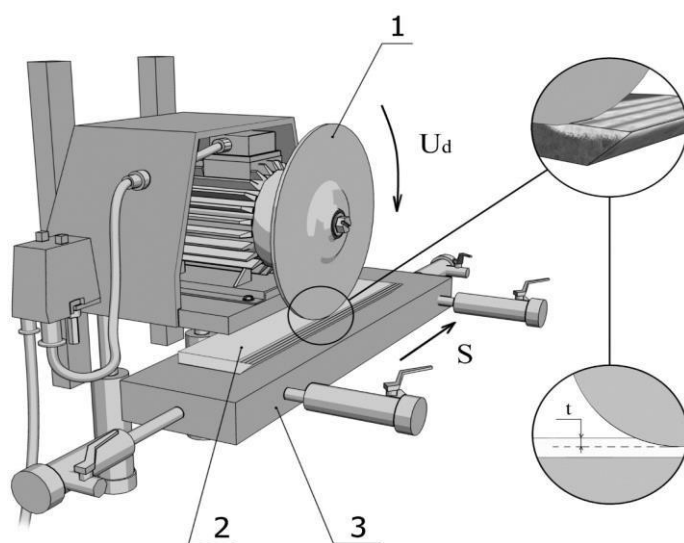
Схема ТФЗ: 1 – різальний диск; 2 – зразок; 3 – магнітна плита верстата
